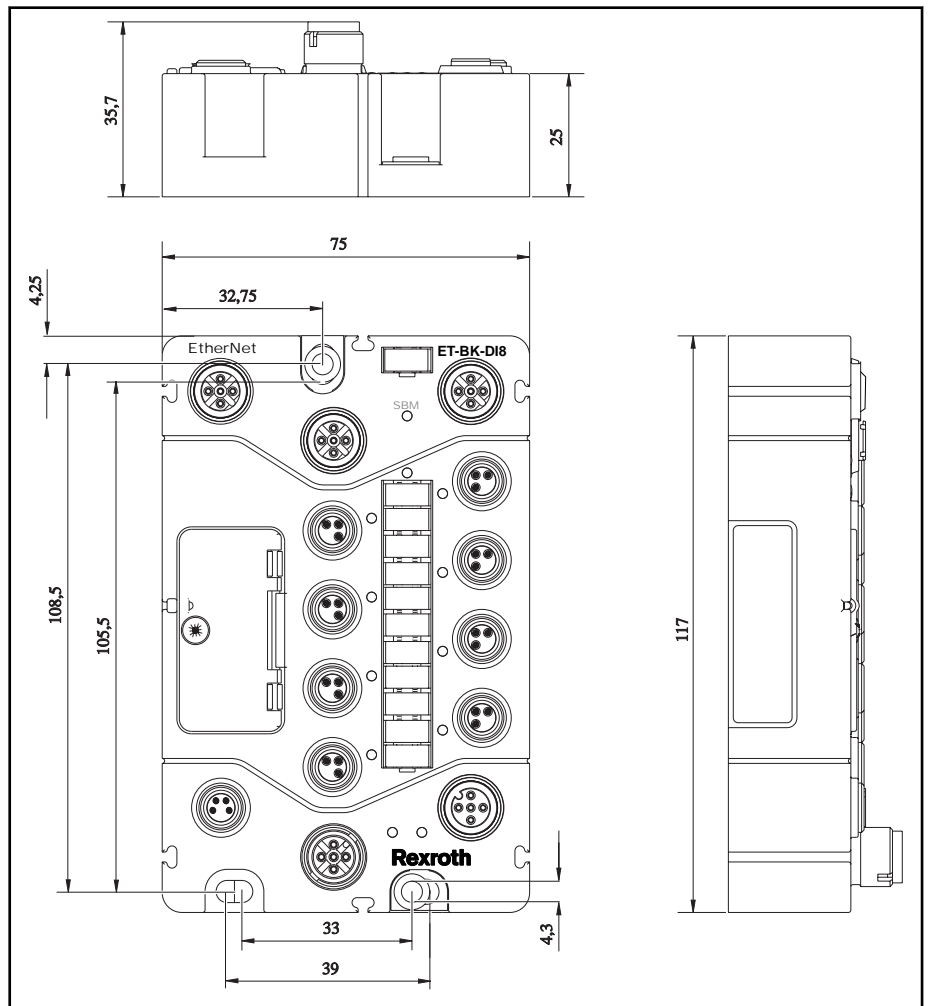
Abmessungen des Feldbus-Kopplers in Millimetern
